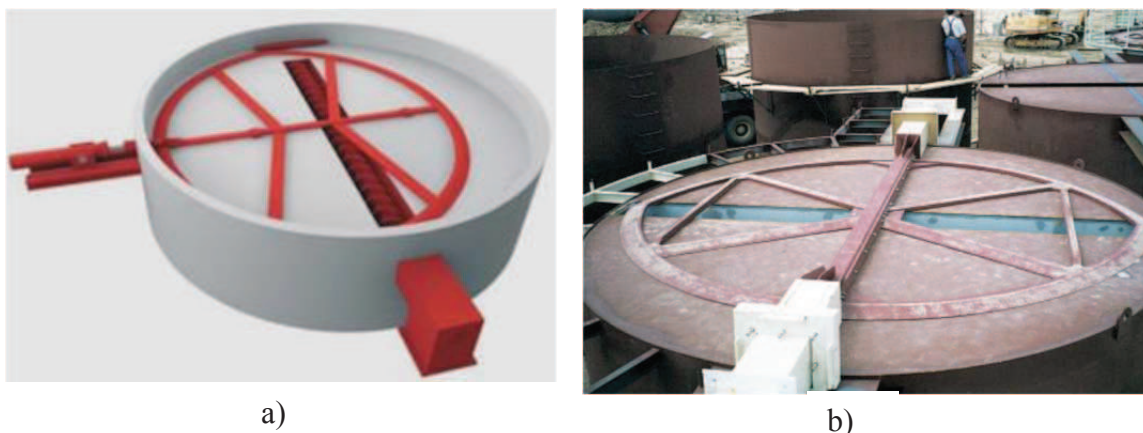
Silo de fondo plano. a) Esquema del mecanismo de arrastre de material, b) Mecanismo de arrastre para silos de fondo plano.
